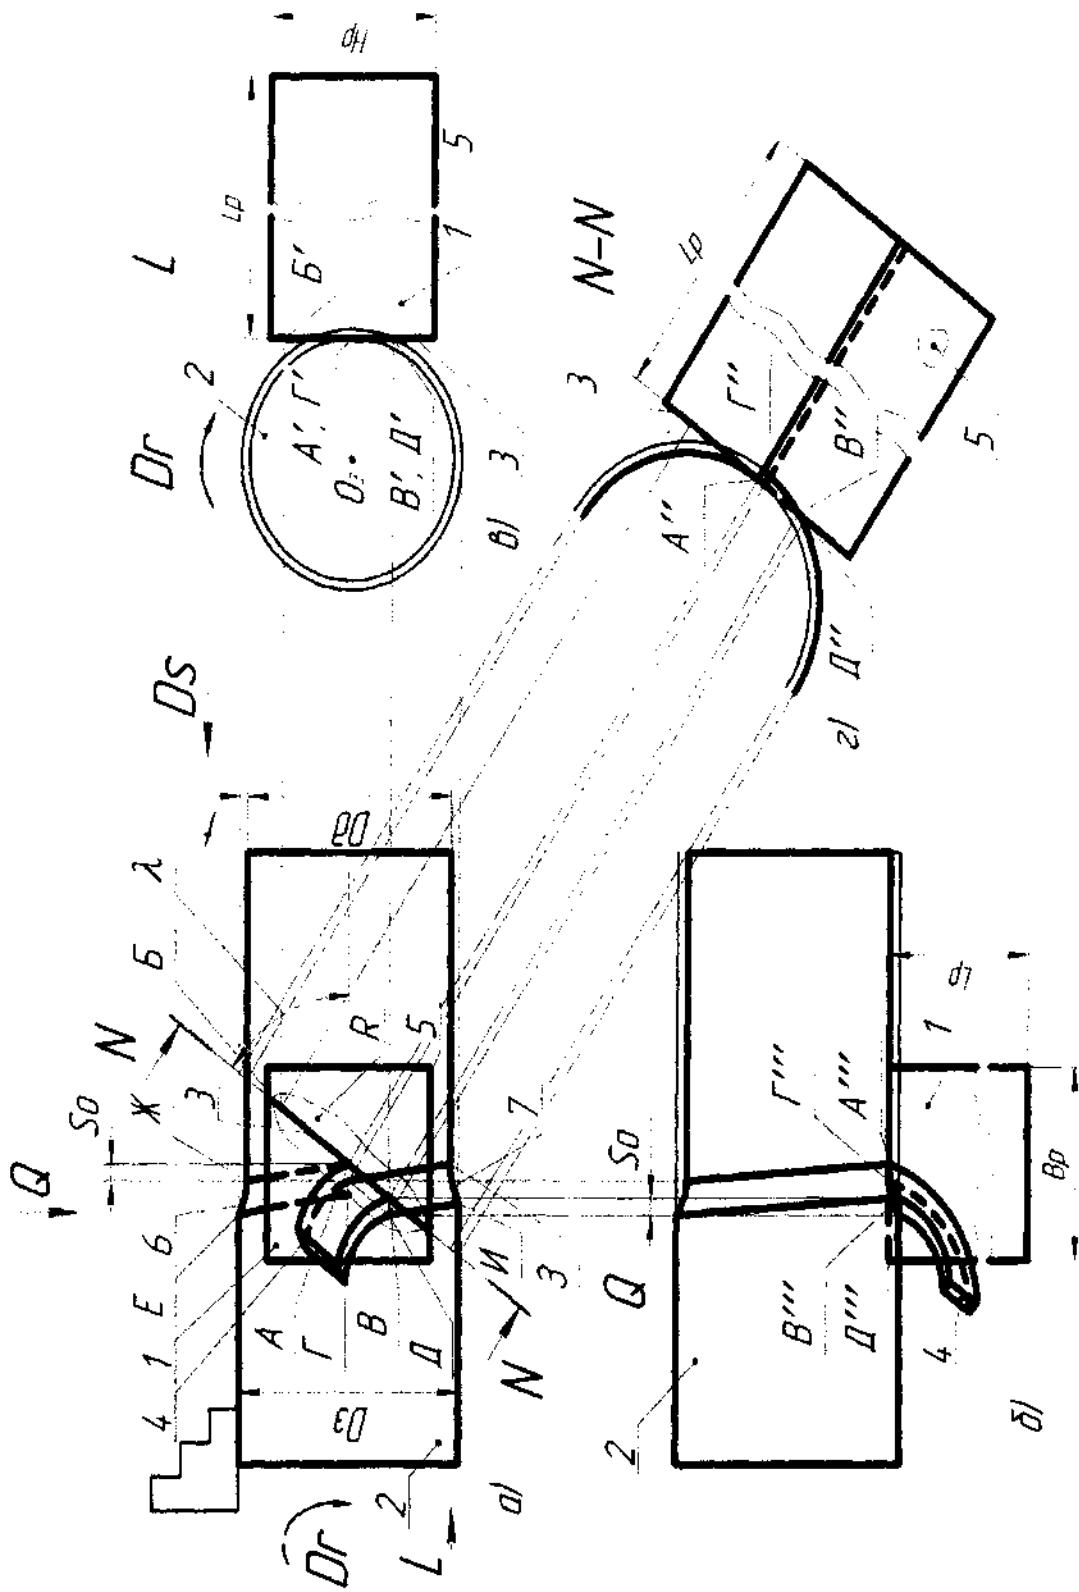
Схема работы токарного проходного безвершинного резца во всех проекциях
